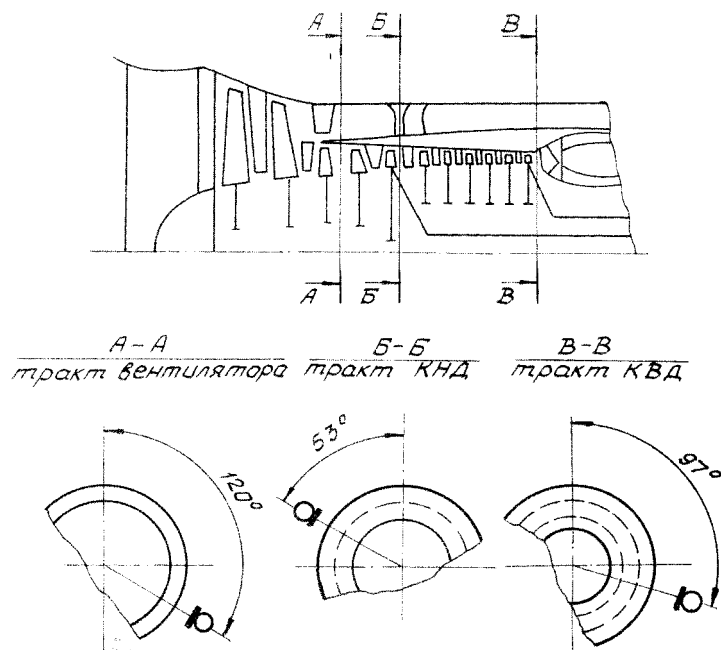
Схема установки устройства для измерения пульсаций давления в проточной части двигателя НК-86
